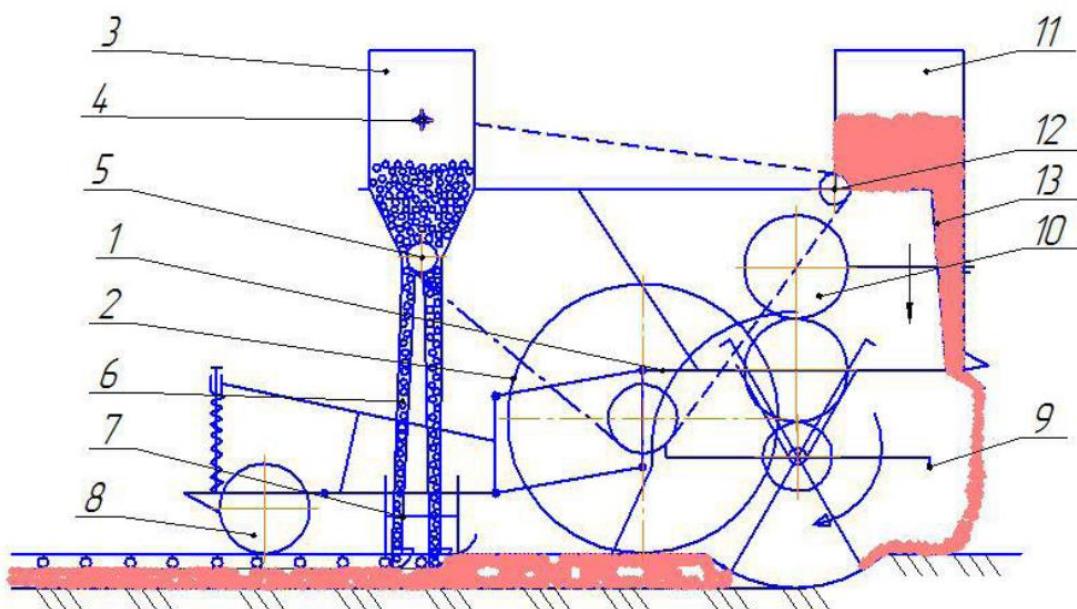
Фреза-селялка: 1-рама; 2-опорно-приводное колесо; 3-семявысыпающий ящик; 4-ворошитель; 5-семявысыпающий аппарат; 6-семяпровод; 7-сошник; 8-каток; 9-фреза; 10-редуктор фрезы; 11-туковывающий аппарат; 12-привод туковысыпающего аппарата; 13-тукопровод
